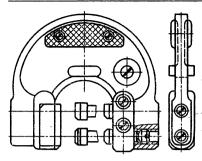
Скоба гладкая, регулируемая, с двумя подвижными вставками и одной неподвижной губкой
